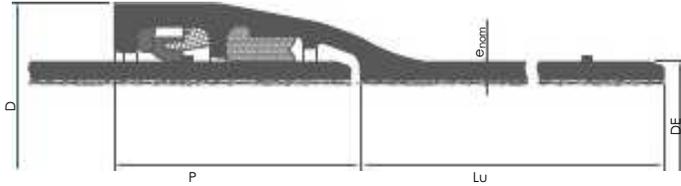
Tubería de hierro dúctil con junta acerrojada Xanchor
